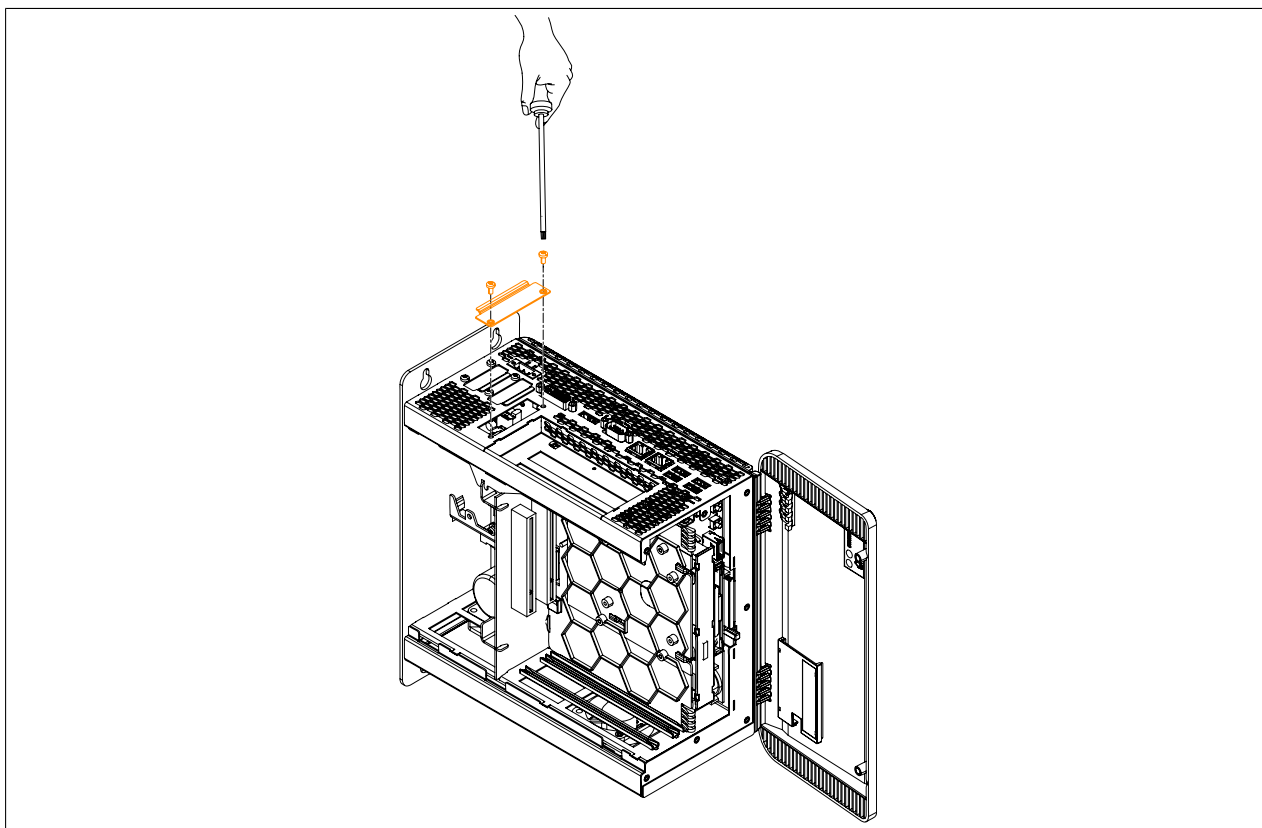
Kombitorxschrauben und Blindabdeckung entfernen
